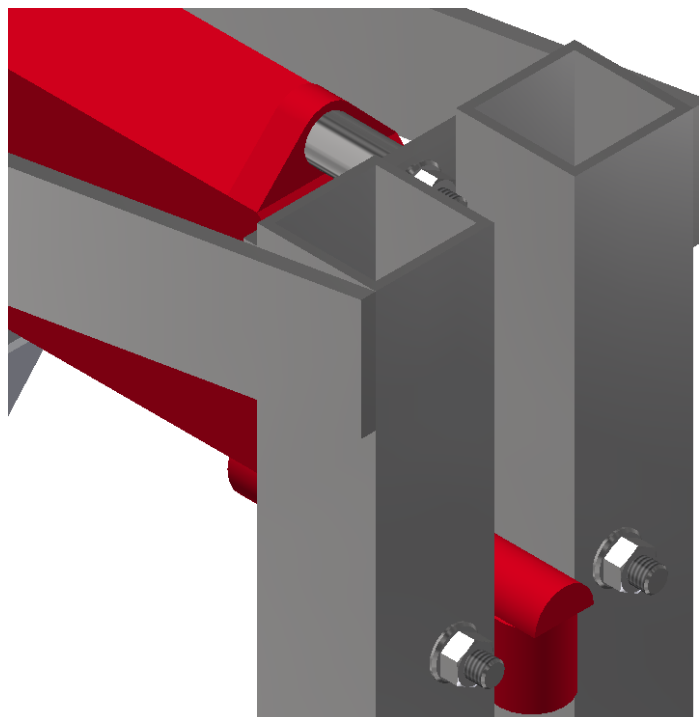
Uchycení pneumatického aktuátoru - pohled 2
